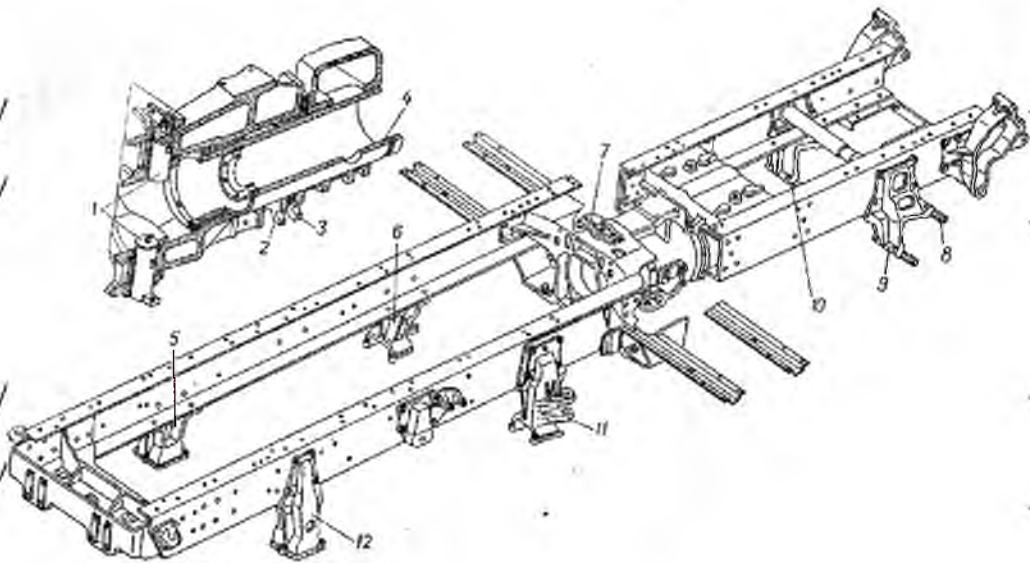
Рама трактора ЛТ-171: 1 — вісь вертикального шарніра; 2 — корпус шарніра; 3 — бугель задньої опори шарніра; 4 — труба горизонтального шарніра; 5 — кронштейн ресори передній правий; 6 — кронштейн ресори задній правий; 7 — кронштейн слідкуючої тяги; 8 — болт; 9 — кронштейн заднього моста лівий; 10 — кронштейн заднього моста правий; 11 — кронштейн ресори задній лівий; 12 — кронштейн ресори передній лівий
